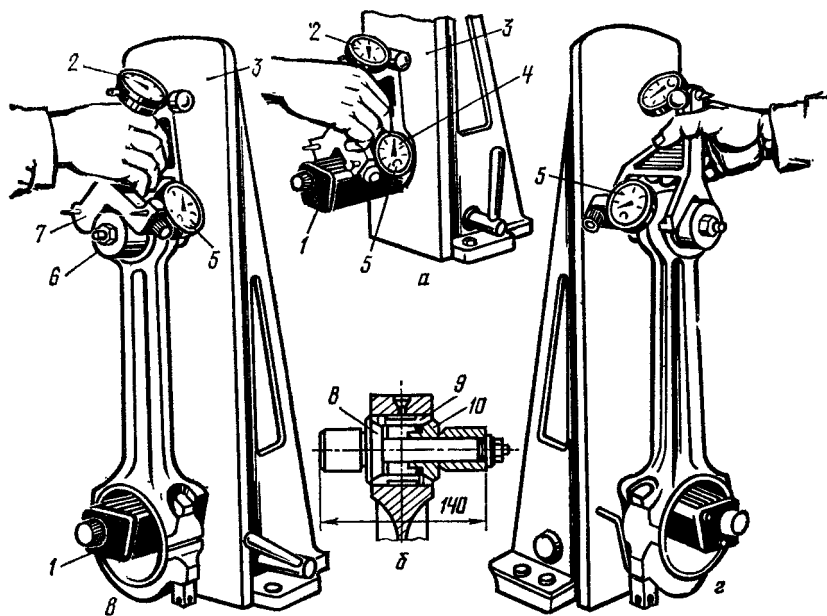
Приспособление для проверки шатуна на скрученность и изгиб:
